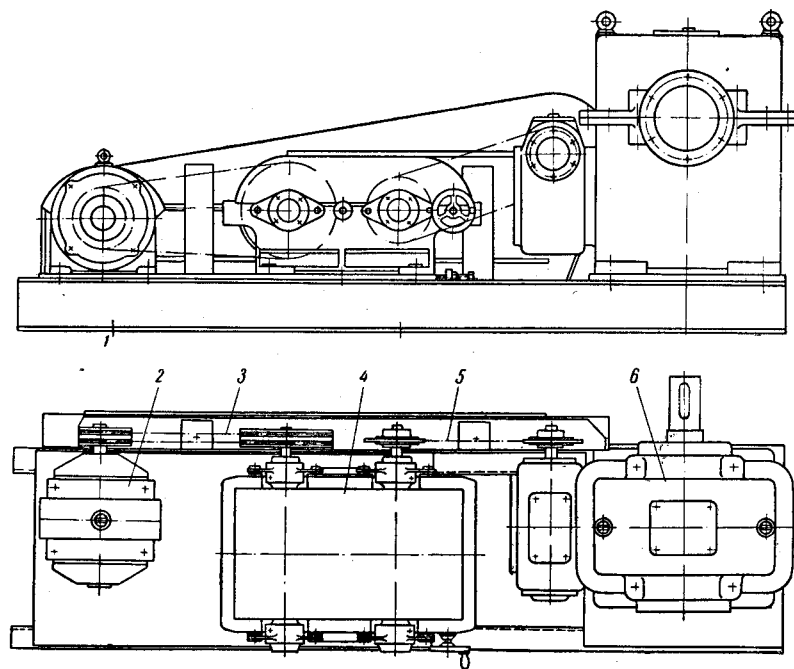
Привод конвейера с двухступенчатым червячным редуктором.
